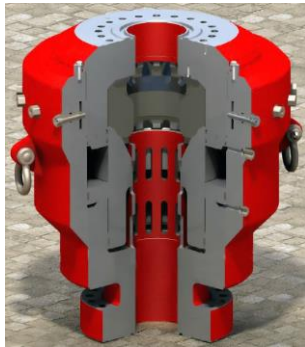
Beispiel für eine Schutzvorrichtung gegen Gasaustritt (Blow Out Preventer)
